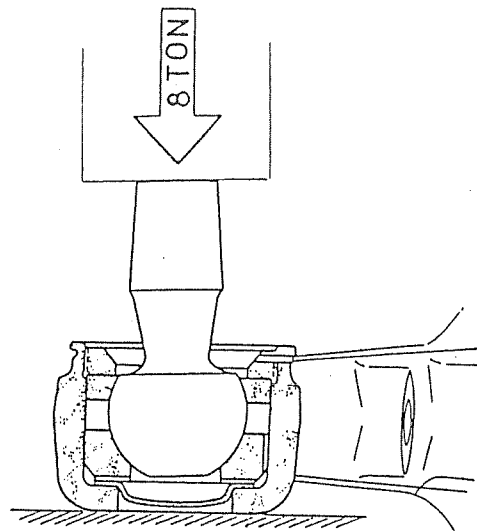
Pressning av kulbult (chassinr. 1-2650).
